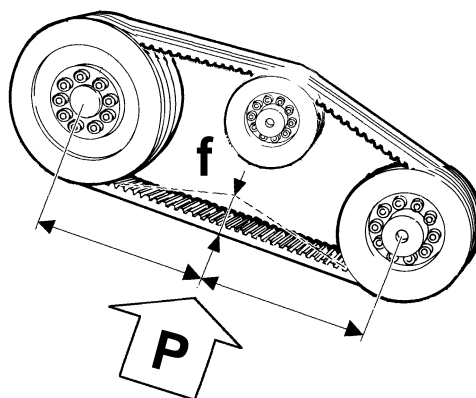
Controllo tensionamento cinghie di trasmissione - Inspection of drive belts tightening
